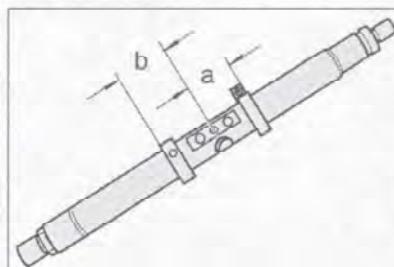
Отрегулируйте измерительное приспособление VW 385/1 на размер *a* = 45 мм. Отрегулируйте установочное кольцо приспособления на размер *b* = 75 мм.
